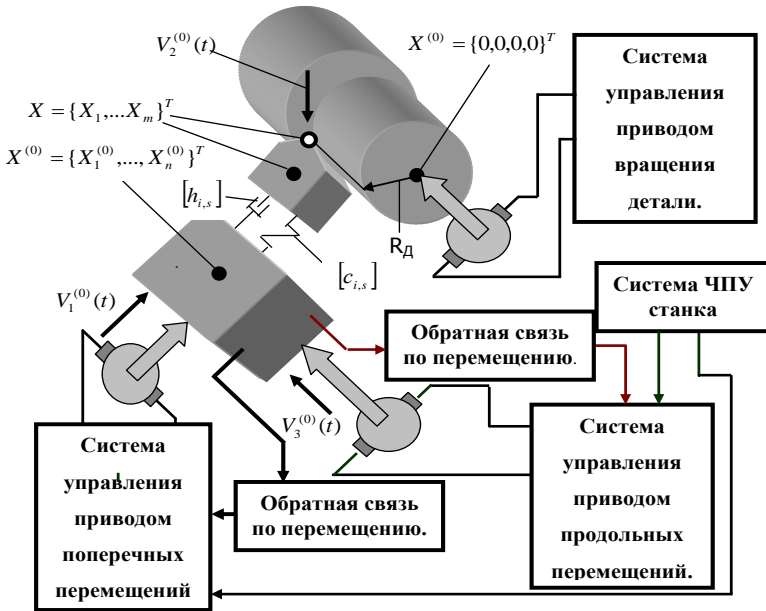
Схема управления формообразующими движениями инструмента относительно заготовки при токарной обработке
